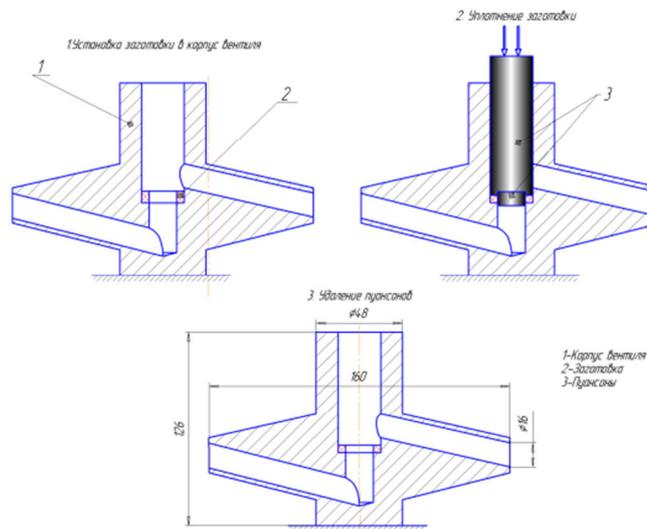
Схема процесса динамического горячего прессования в заготовке корпуса вентиля
